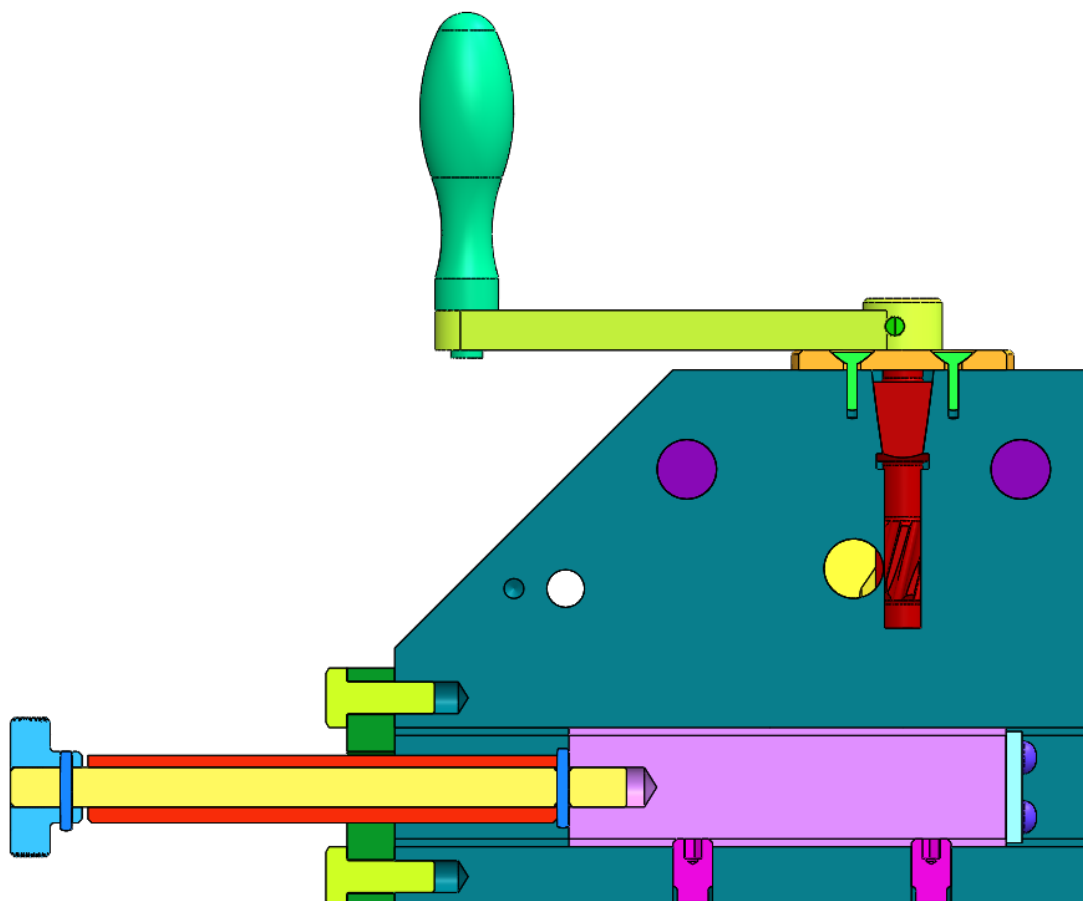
Кондуктор универсальный для сверления отверстий в осях
